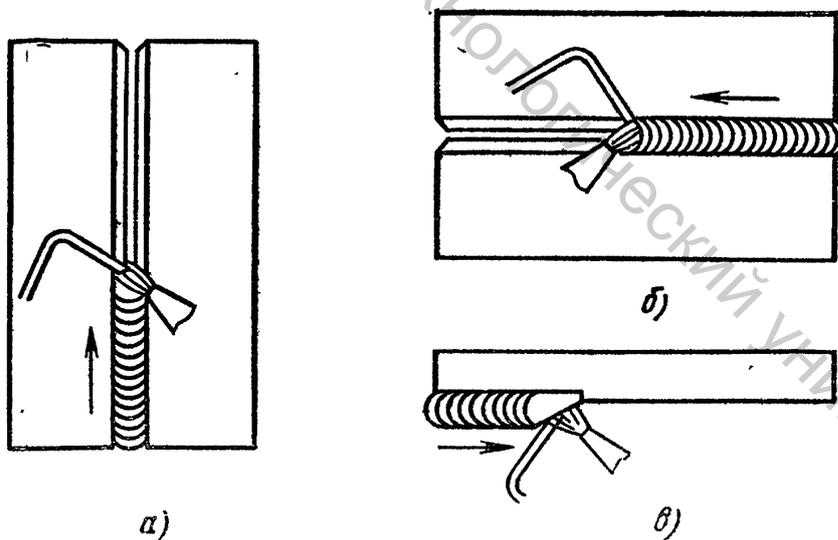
Схемы горизонтального и вертикального способов сварки
